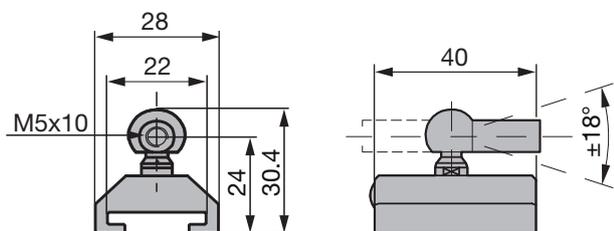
Dimensions de montage du capteur de position BTL5-F-2814-1S
